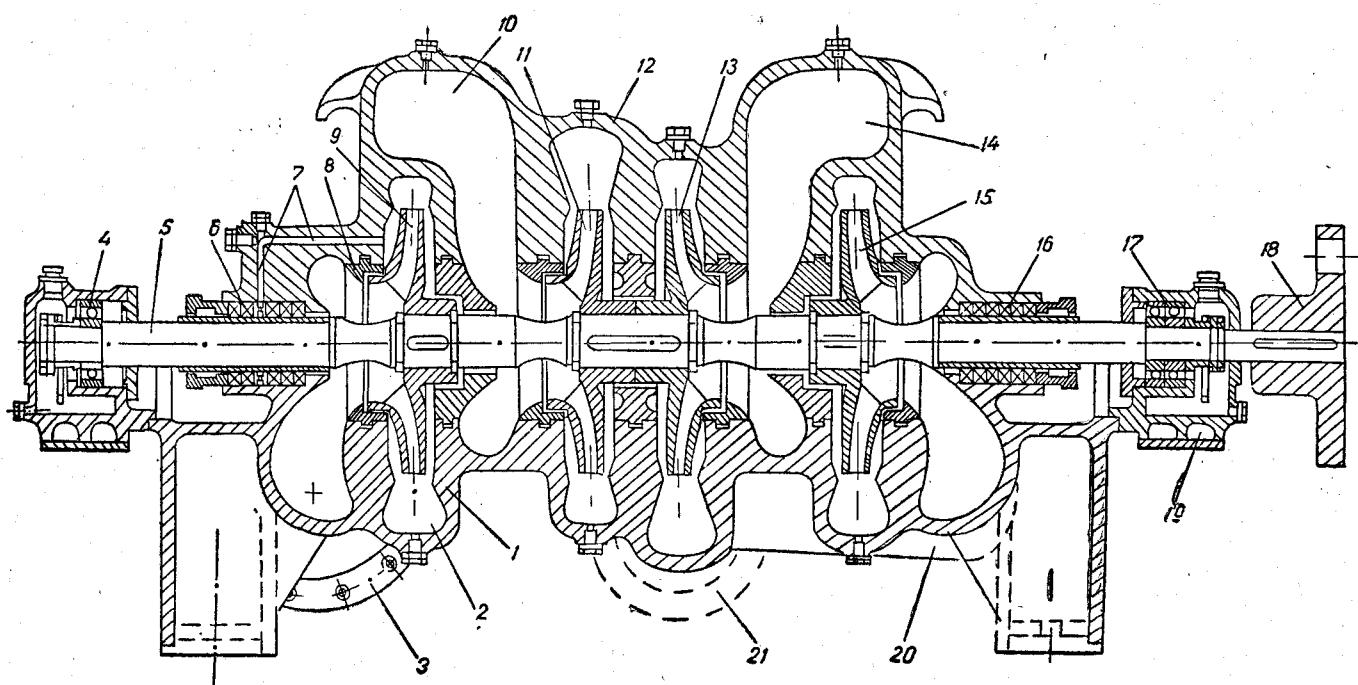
Схема четырехколесного центробежного насоса с горизонтальным разъемом корпуса:
